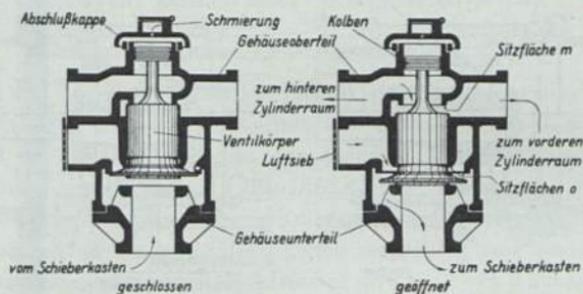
Vereinigtes Zylindersaug- und Druckausgleichventil
